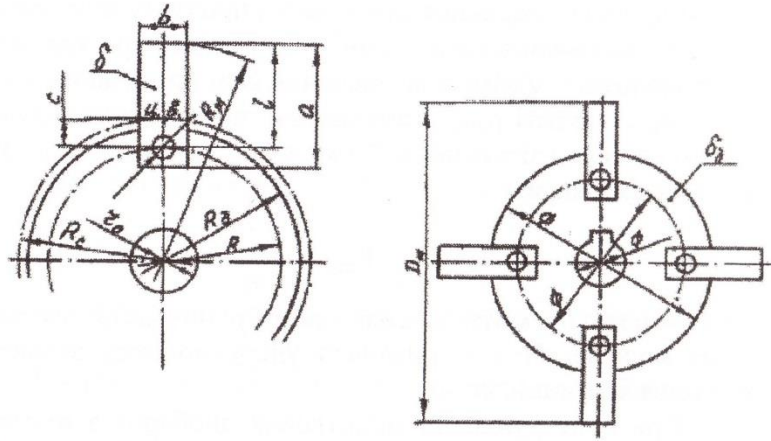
Розрахункова схема елементів молоткової дробарки.
